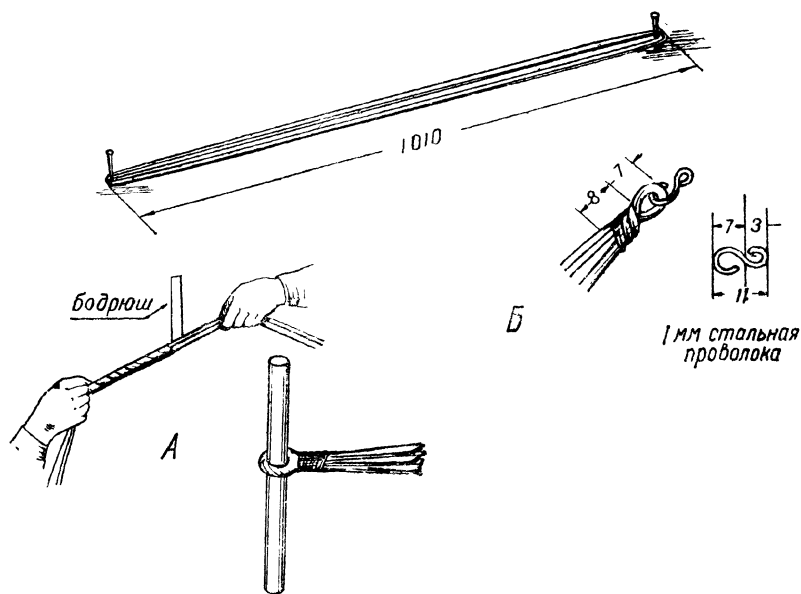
Изготовление резиноmotorа: А — заправка концов резиноmotorа; Б — конец резиноmotorа, надеваемый на костыль
